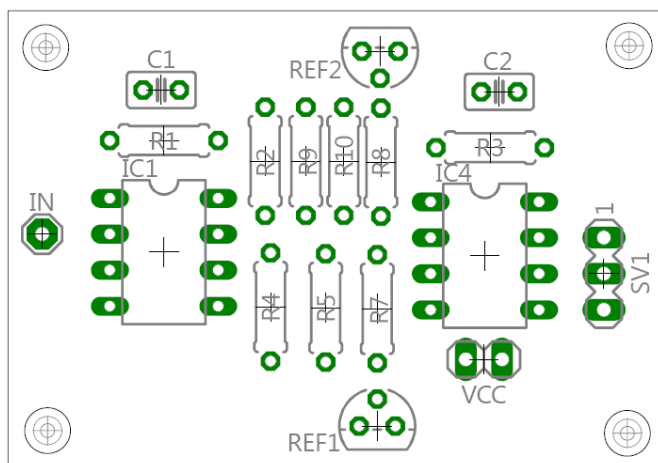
Zobrazení osazení součástek DPS při pohledu BOTTOM
